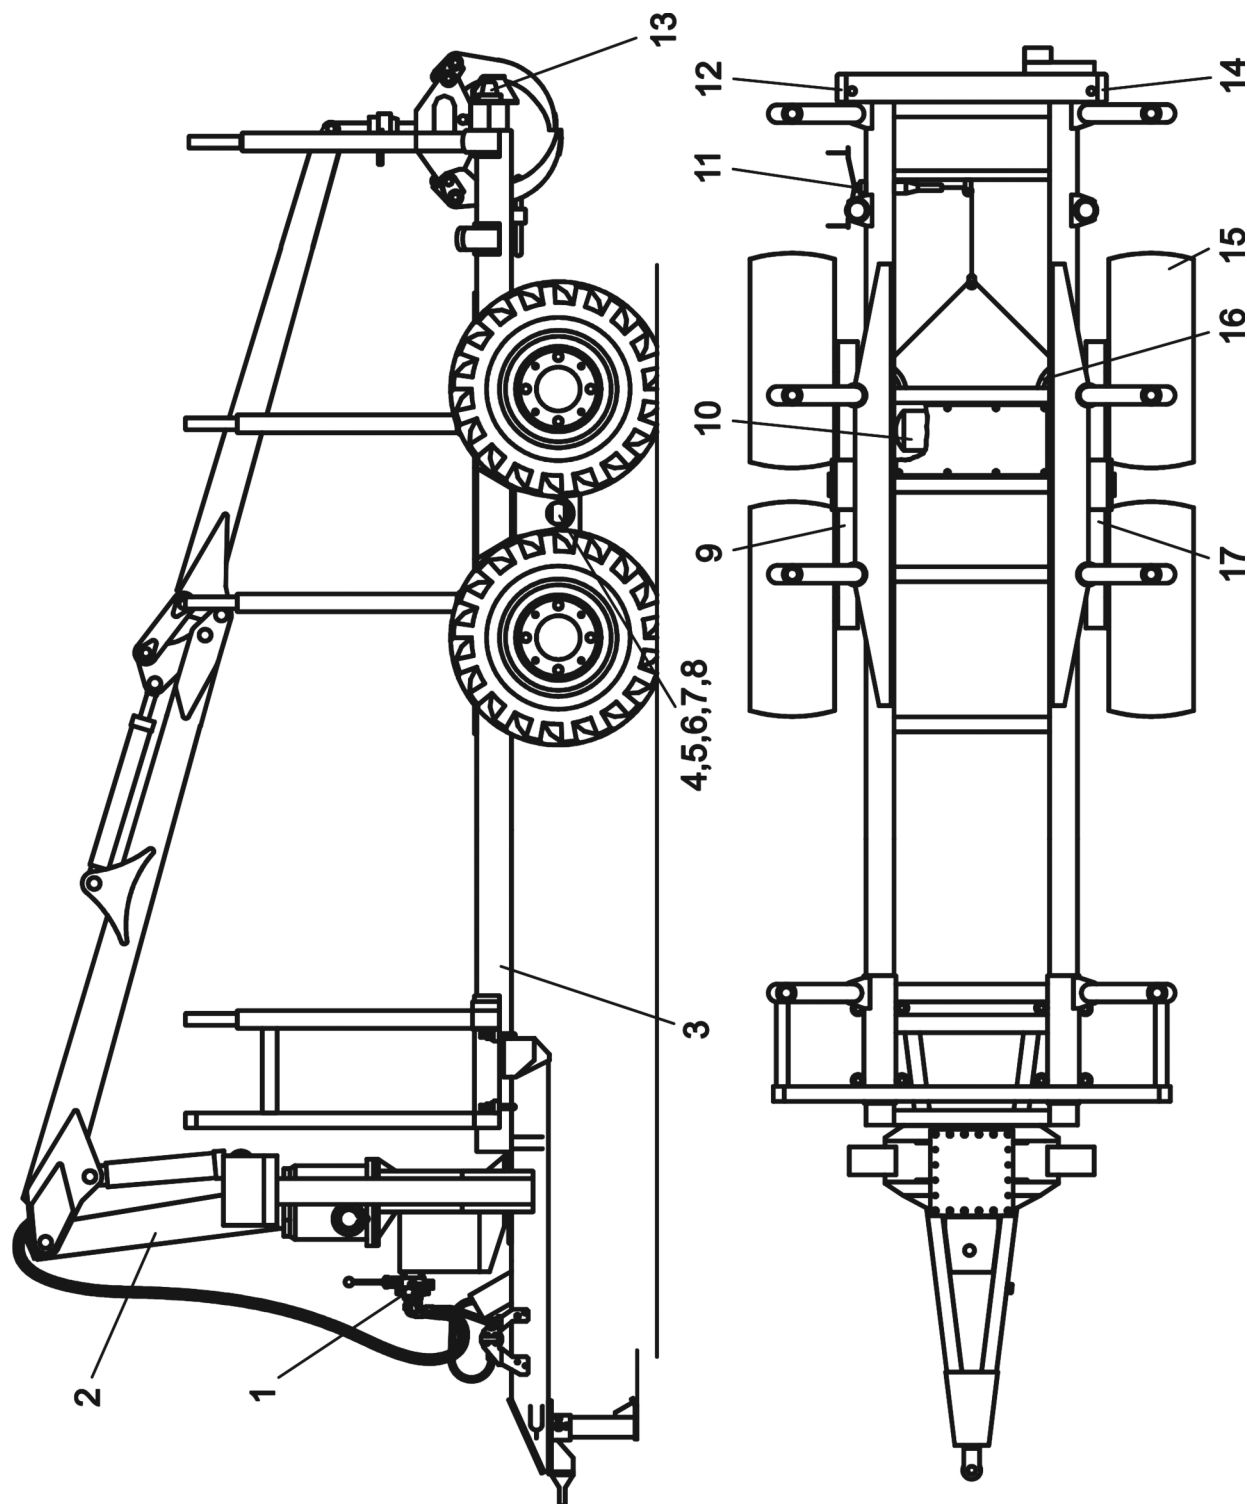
Полуприцеп лесовозный ПЛ-9
